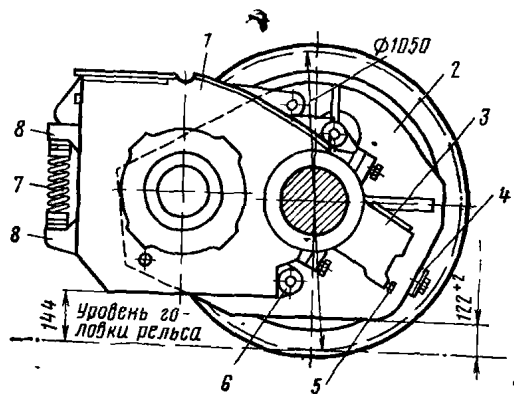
Колесно-моторный блок с осевой подвеской тягового двигателя:
